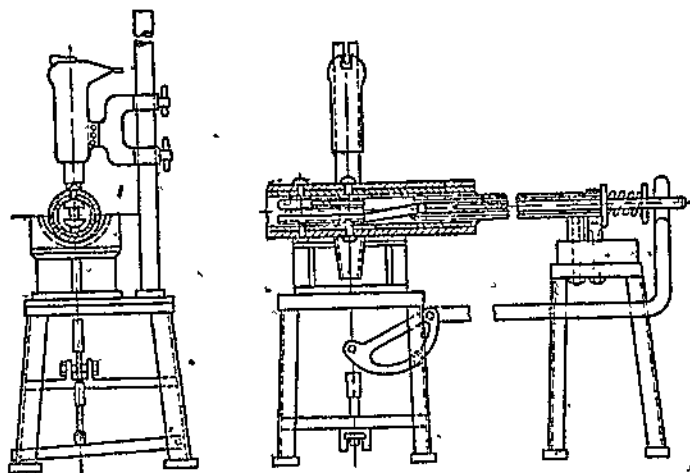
Кондуктор со съемными втулками для растачивания или развертывания отверстий и торцевания втулок уха.
